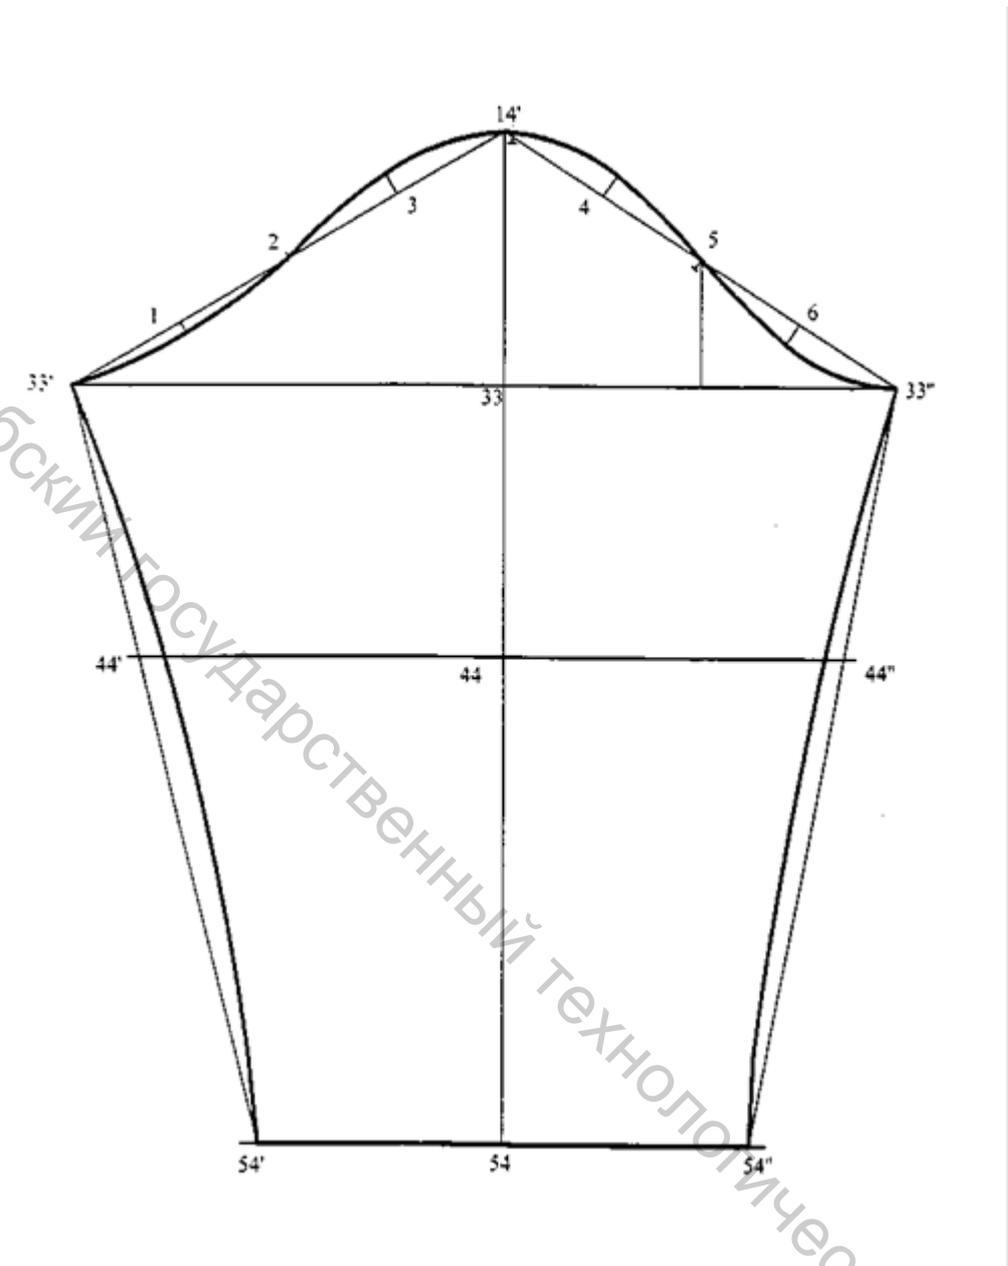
Чертеж базовой и исходной модельной конструкции рукава куртки
